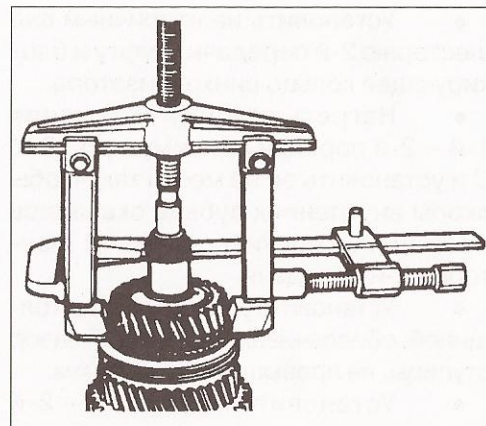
Использование специального приспособления для снятия шестерни 4-й передачи.
